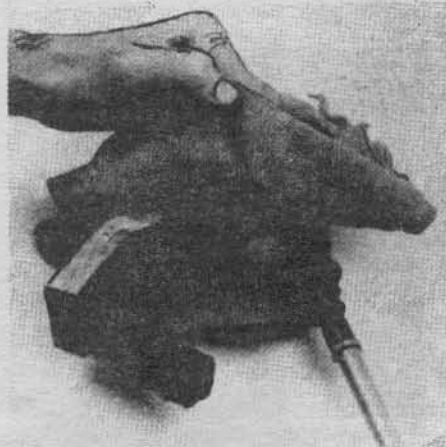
Выпрессовка поршня сжатым воздухом. Осторожно, не повредите руги!
